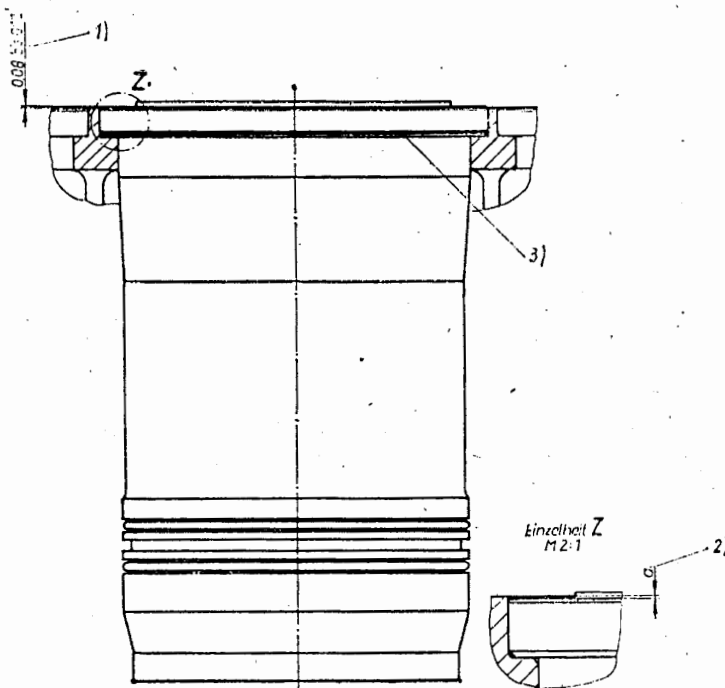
Richtige Zylinderlaufbuchsenmontage
